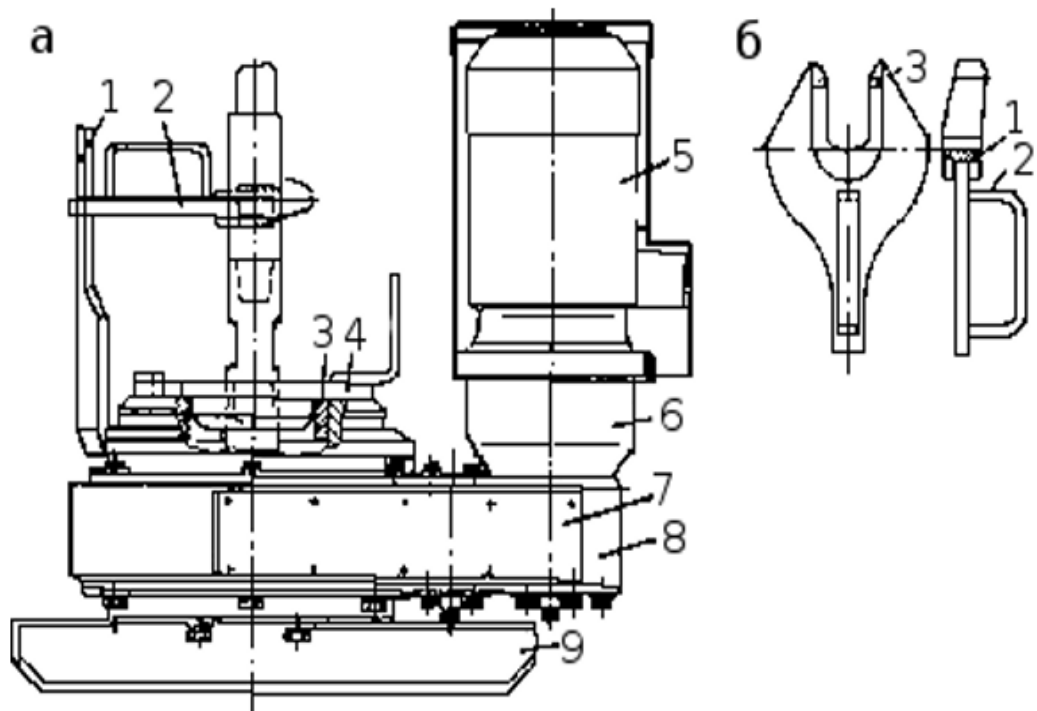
Схема трубозворота РТ-1200М:
